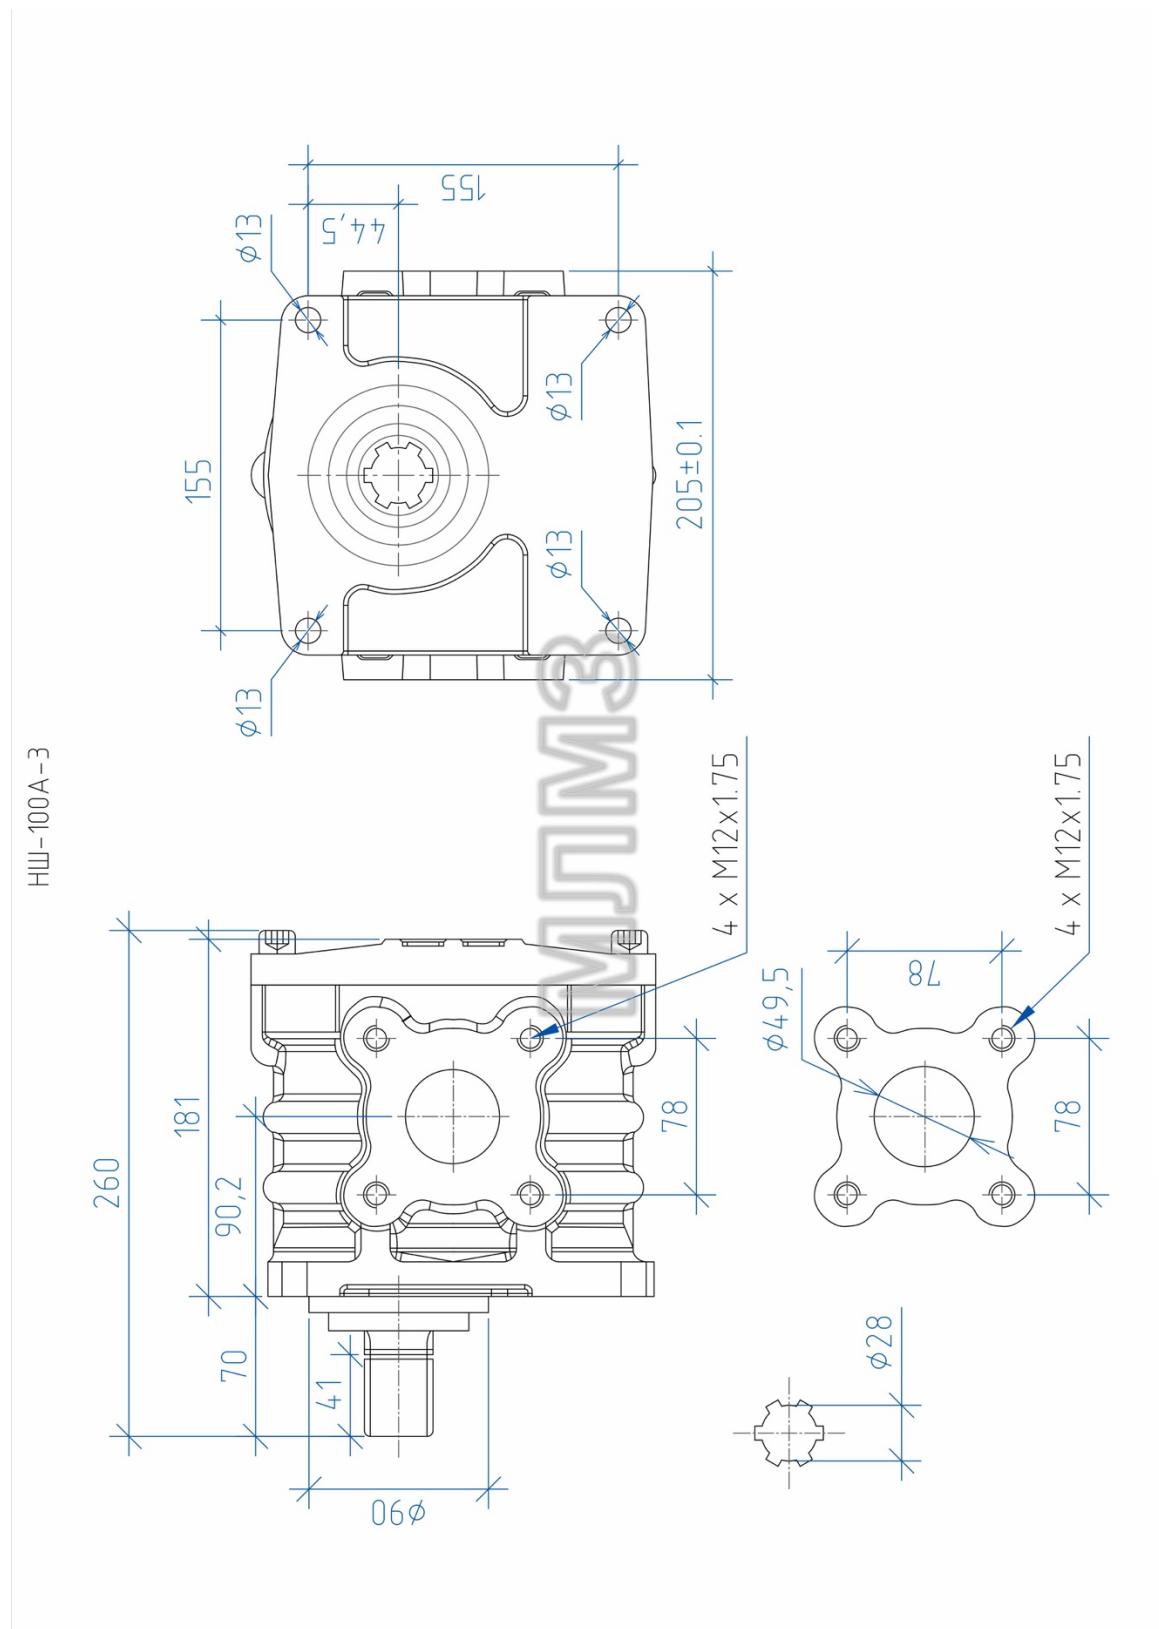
Насосы шестеренные НШ100А-3, НШ100А-3Л. Габаритные и присоединительные размеры.
